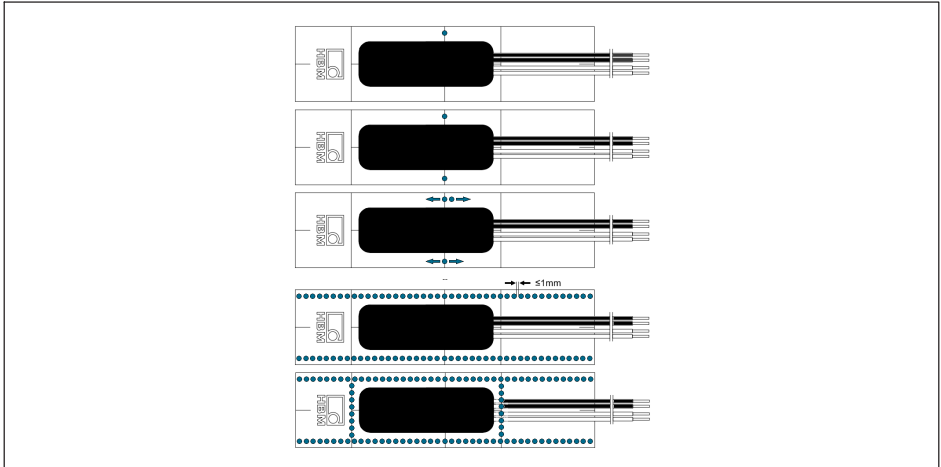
Séquence de soudage de la LS31 HT
